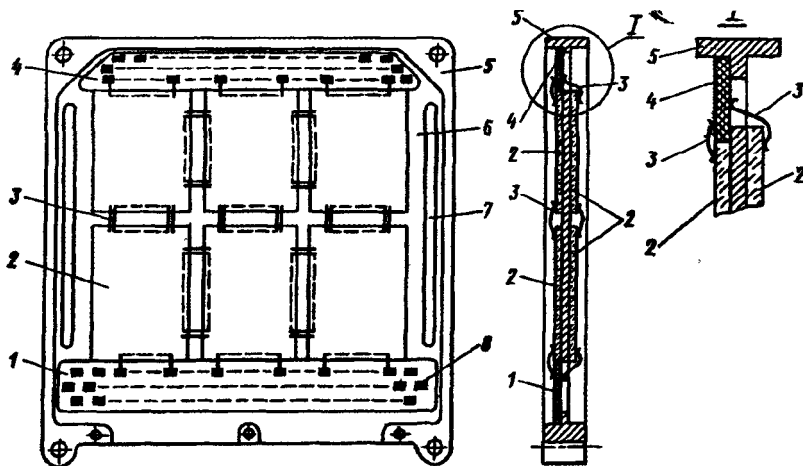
Конструкция двухсторонней ФЯ на металлической рамке:
